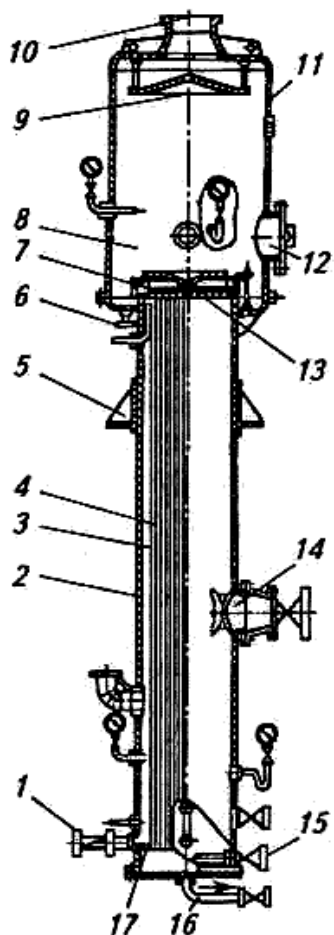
Предварительный трубчатый пленочный дистиллятор: 1 — патрубок для отвода конденсата пара; 2 — корпус нагревательной секции; 3 — нагревательная секция; 4 — пучок нагревательных трубок; 5 — лапы; 6 — патрубок для отвода упаренной мисцеллы; 7 — сепаратор; 8 — сепарационная секция; 9 — каплеотражатель; 10 — патрубок для паров растворителя; 11 — корпус сепарационной секции; 12 — люк; 13, 17 — верхняя и нижняя трубные решетки; 14, 15 — патрубки для подвода водяного пара и мисцеллы; 16 — патрубок для слива мисцеллы из аппарата
